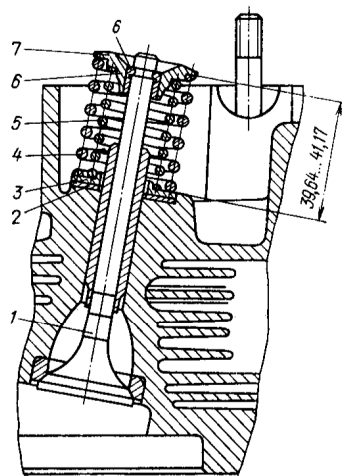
Восстановление усилия клапанных пружин способом установки дополнительной шайбы:
